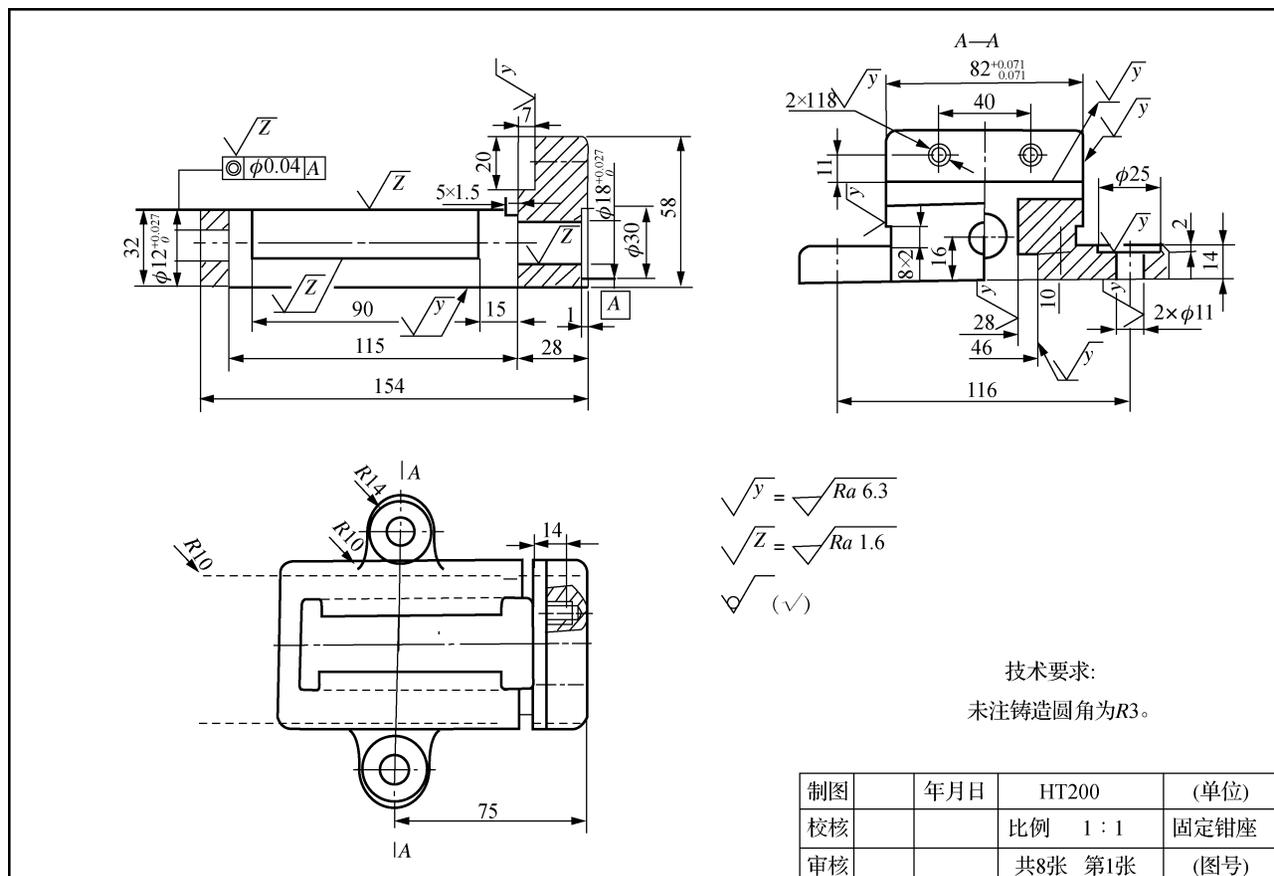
机用台虎钳 1 号零件固定钳座零件图
